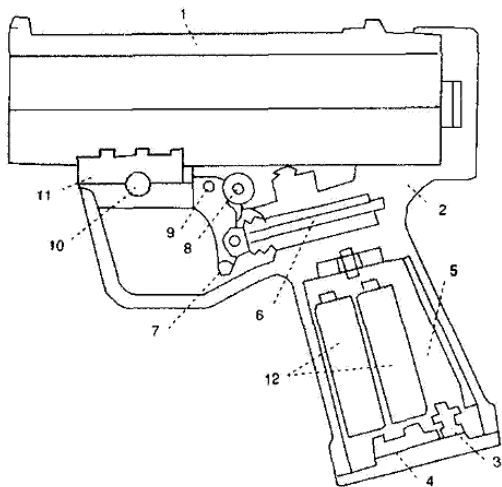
Схема общего устройства пистолета Р-11: 1. Блок стволов; 2. Рукоятка; 3. Разъем для подключения контрольно-проверочного прибора; 4. Винт крепления блока питания; 5. Блок питания; 6. Выключатель; 7. Спусковой крючок; 8. Предохранитель; 9. Штифт крепления спускового крючка; 10. Штифт крепления блока стволов; 11. Кронштейн крепления блока стволов; 12. Батареи блока питания.
